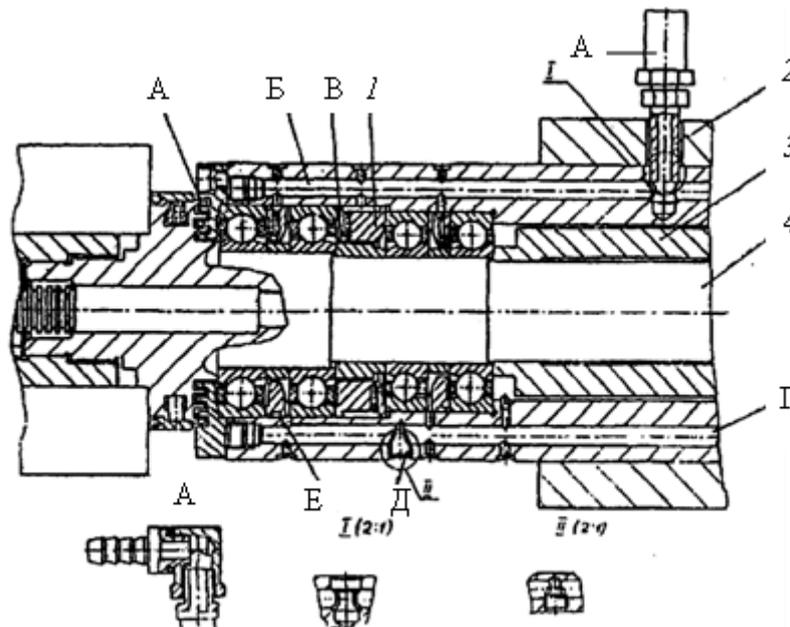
Передняя опора шпинделя внутришлифовального станка
